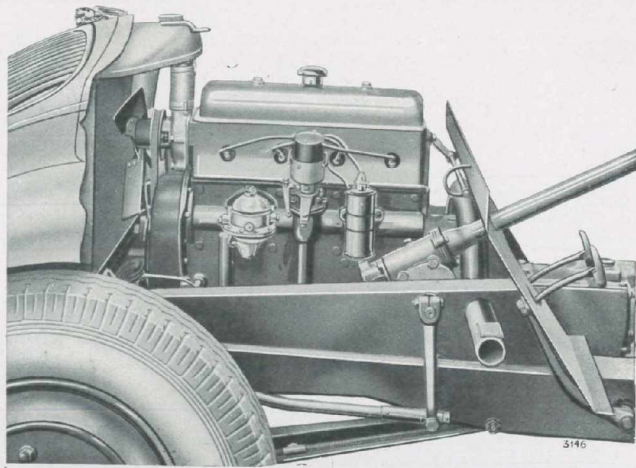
LINKE SEITENANSICHT VOM MOTOR
